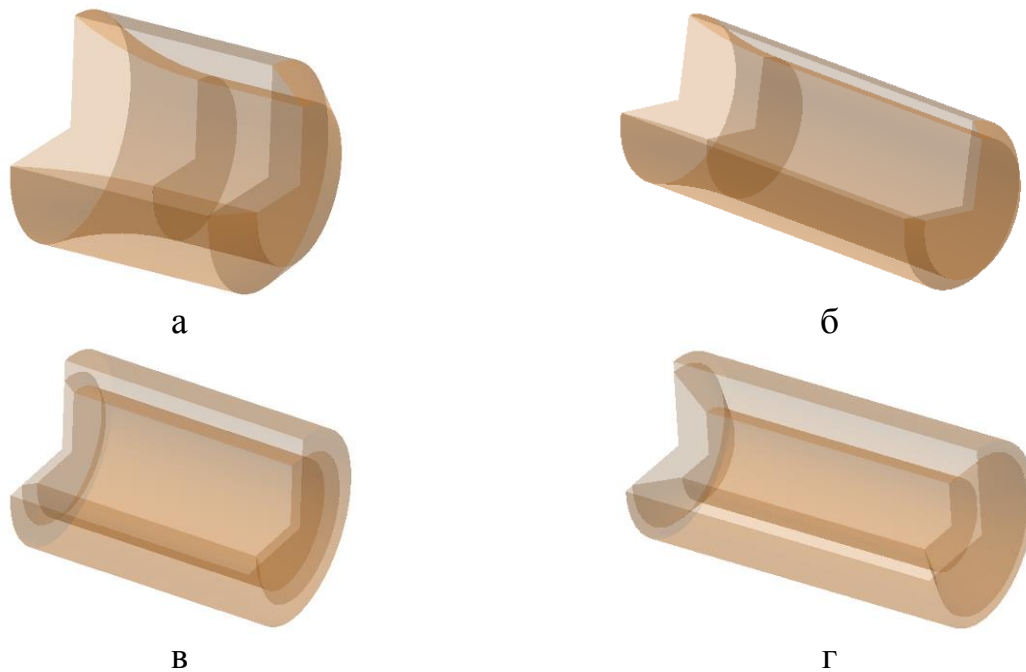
Форми параметричних 3D-моделей: а, б - «оболонка валу з шліцьовою ділянкою»; в, г - «оболонка отвору з шліцями»
